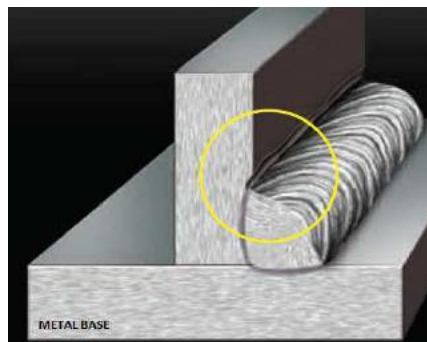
Socavamiento cordón de soldadura [4].
